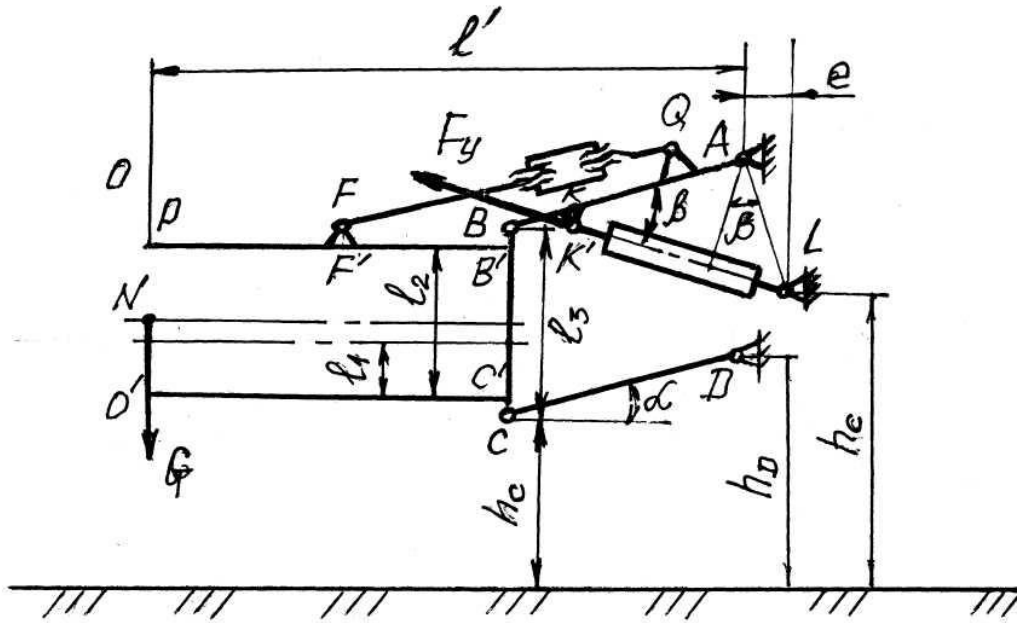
Схема механізму навіски рами ротора струшувача
